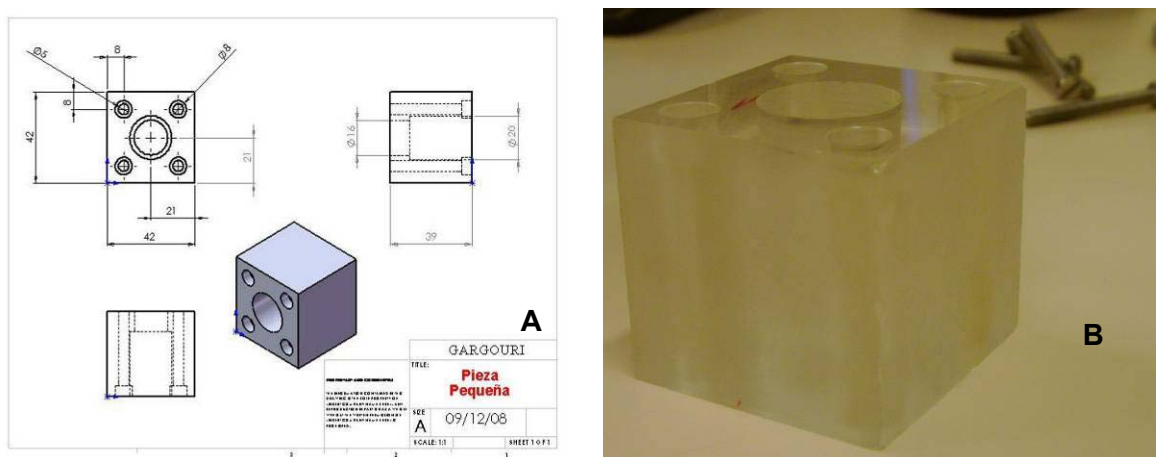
(A) Vistas y dimensiones de una de las piezas del montaje destinada a embutir un palpador: pieza pequeña (se utiliza dos veces), (B) Foto de la pieza pequeña.
